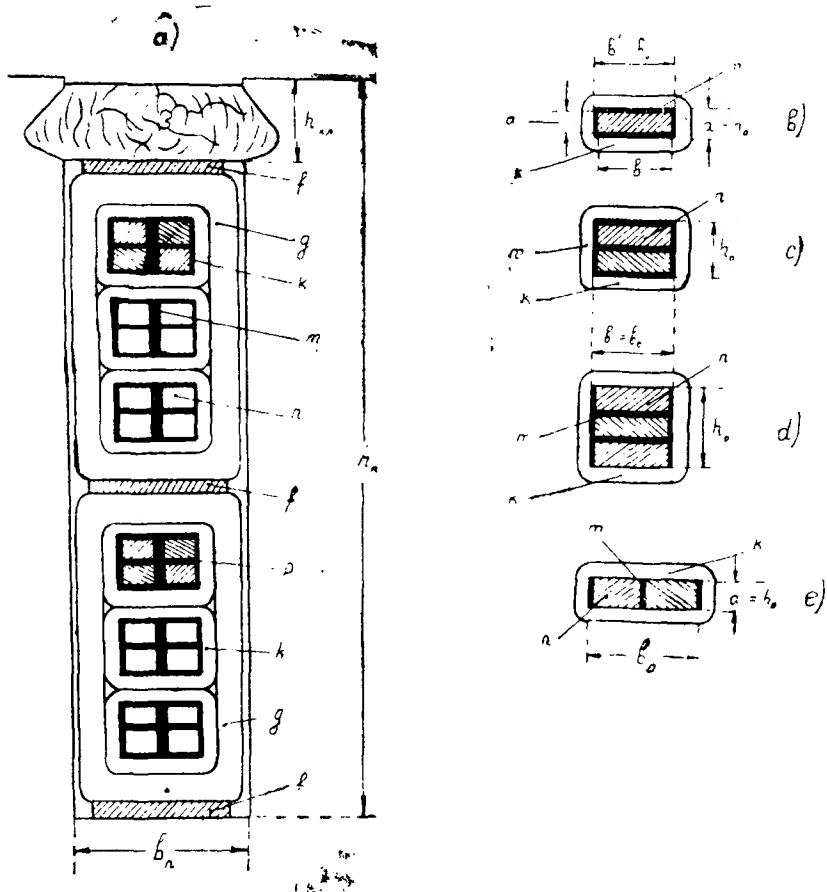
Эскизы витковой и корпусной изоляции двухслойной катушечной обмотки.
